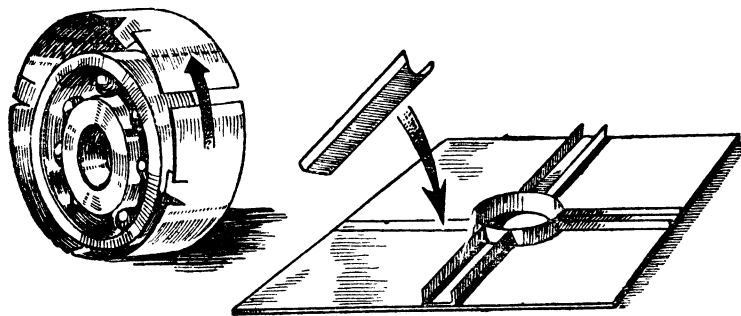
Обойма шарикоподшипника и приспособление для сборки крестовин.
